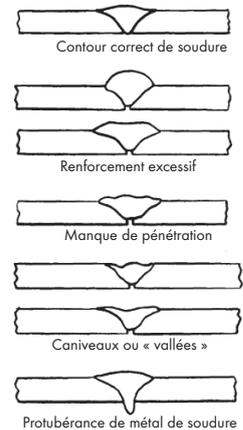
Caractéristiques des bons et des mauvais joints de soudure
